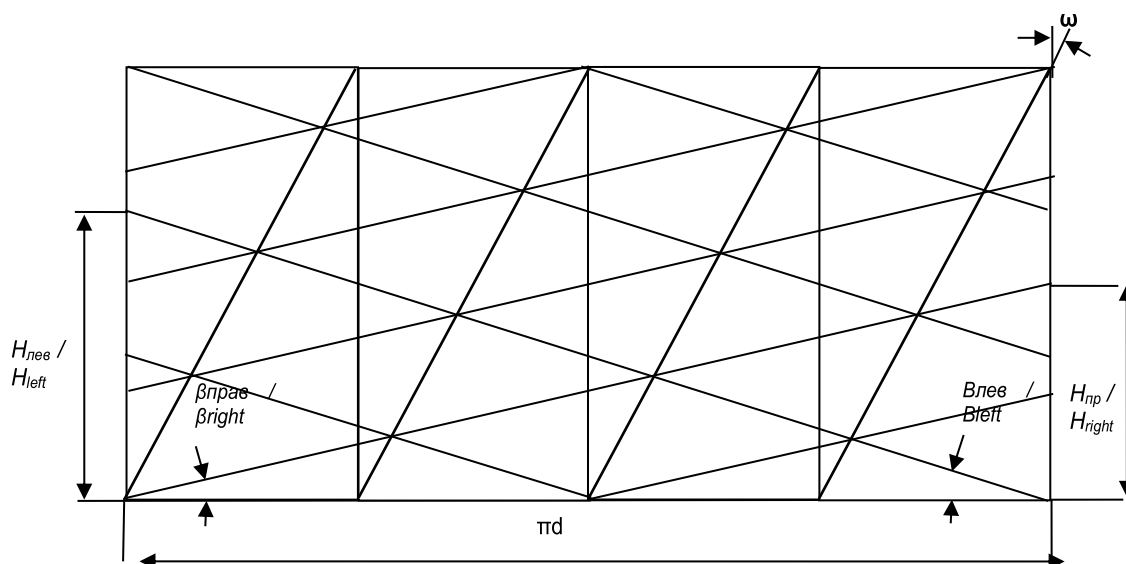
Схема образования переменной схемы резания на острозаточенных фрезях вспомогательными винтовыми поверхностями правого и левого направлений
